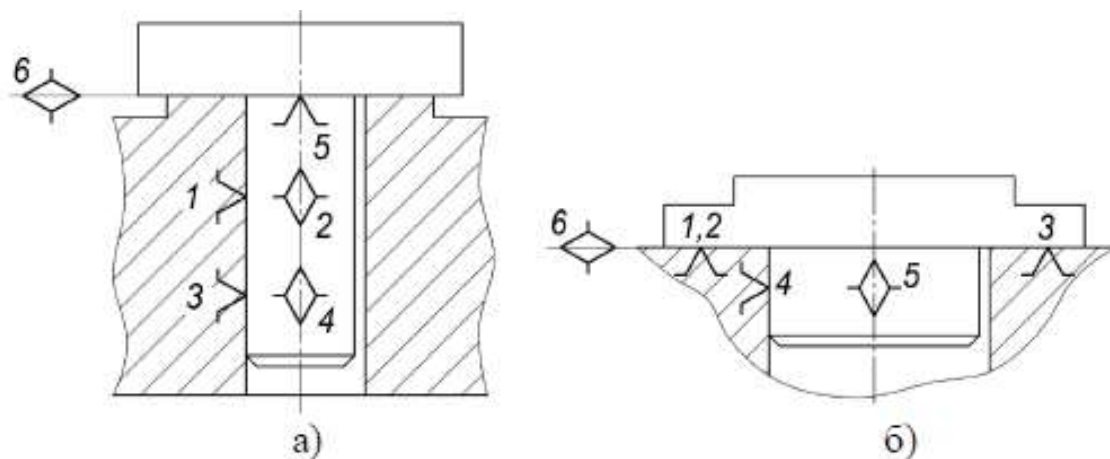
Схеми базування на зовнішній циліндричній поверхні
